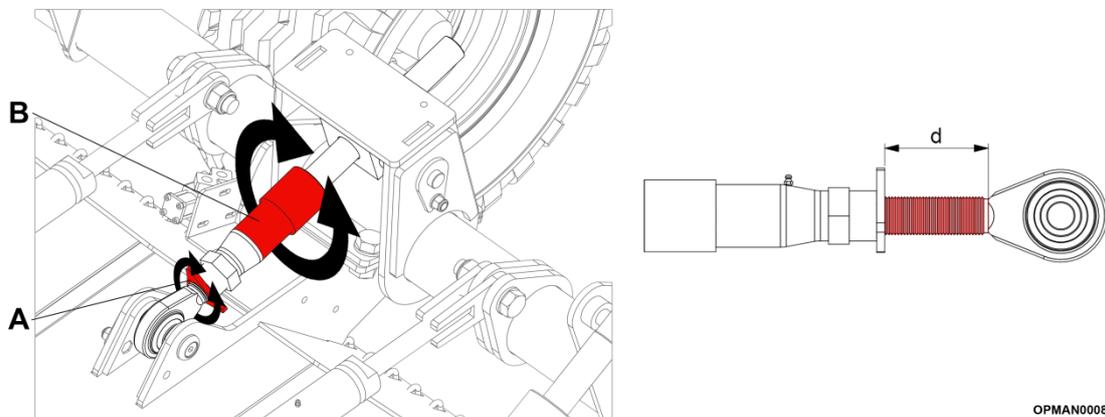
Multicut 820 Minimaler Höhenanschlag
